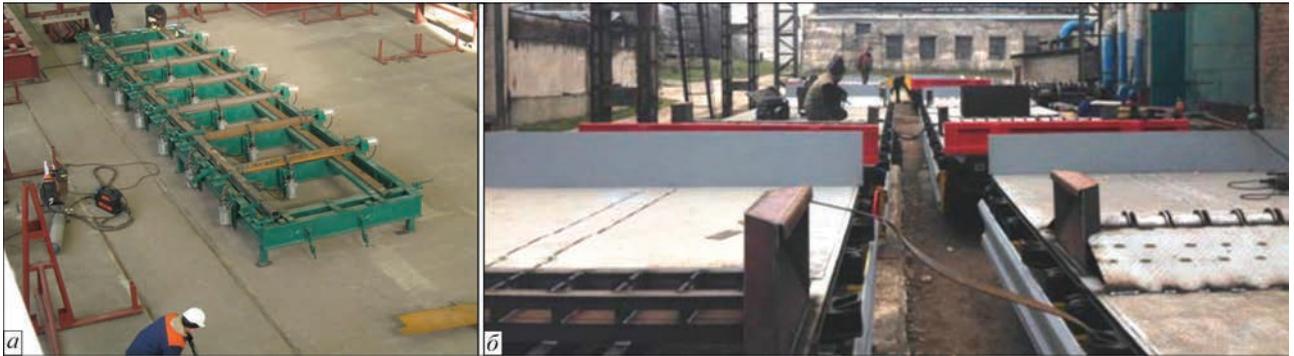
Типичные объекты применения сварки порошковыми проволоками: а — сборка-сварка каркаса боковой стенки грузовых вагонов (ООО «Югпромтехмонтаж», г. Херсон) [15]; б — сварка металлоконструкций платформы для перевозки слябов, рельсов (ПАО «Верхнеднепровский машиностроительный завод»)
